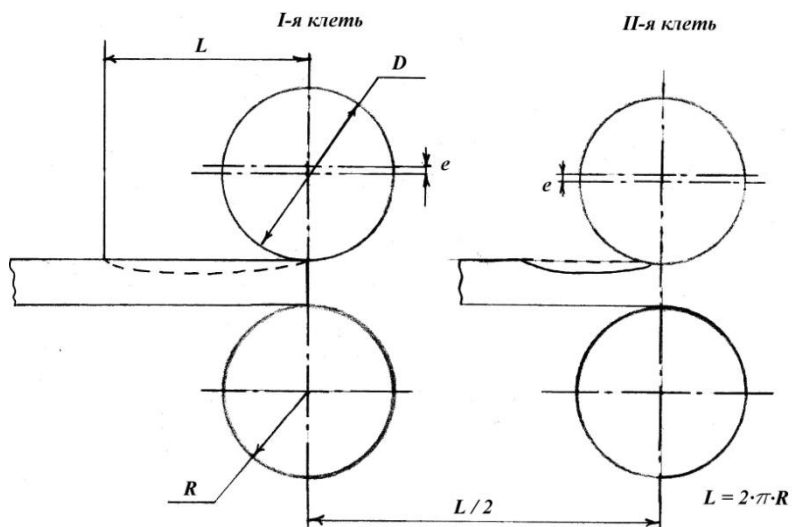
Предлагаемая схема циклической деформации заготовки: R - радиус валков; D - диаметр валков; e - эксцентриситет верхнего валка; L - длина окружности валка;  $L/2$  - расстояние между первой и второй клетью
